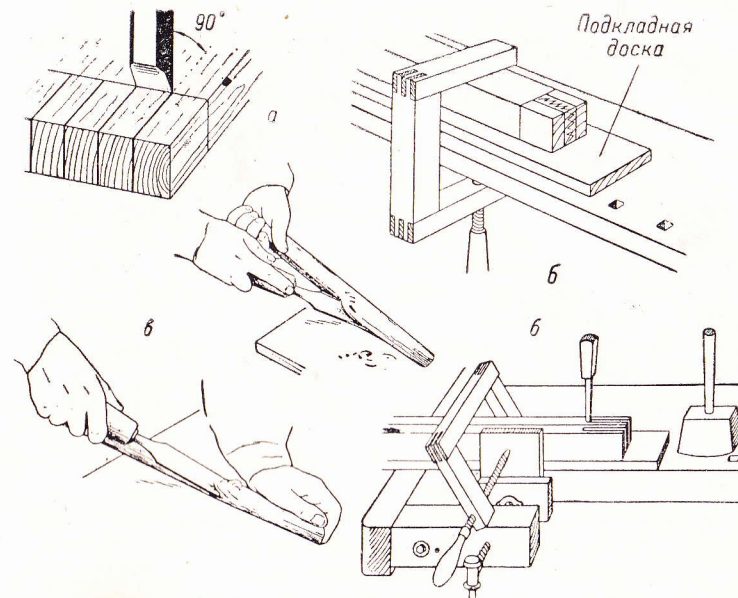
Приемы работы стамесками: а — положение стамески (долота) при долблении; б — закрепление деталей при долблении; в — нельзя держать руку перед инструментом.
